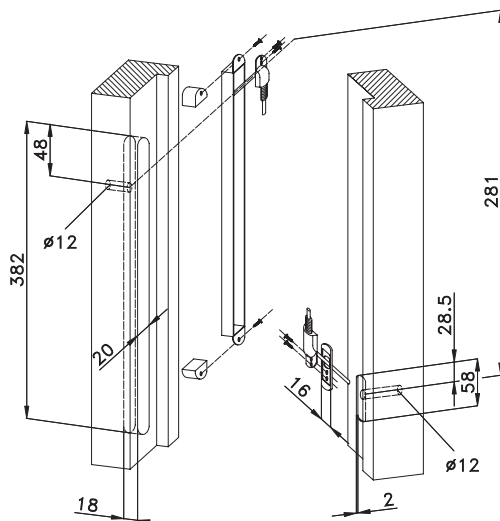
Montaje en madera (medidas en mm)
